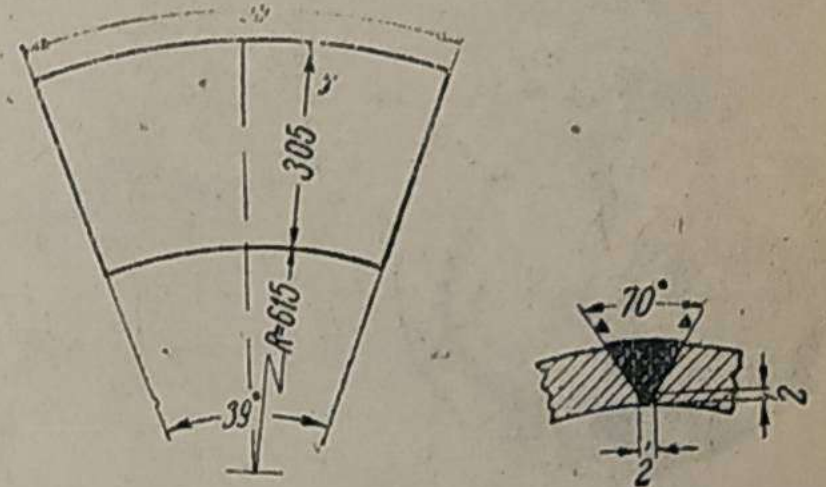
Развертка конуса камеры газификации и сечение сварного шва.
